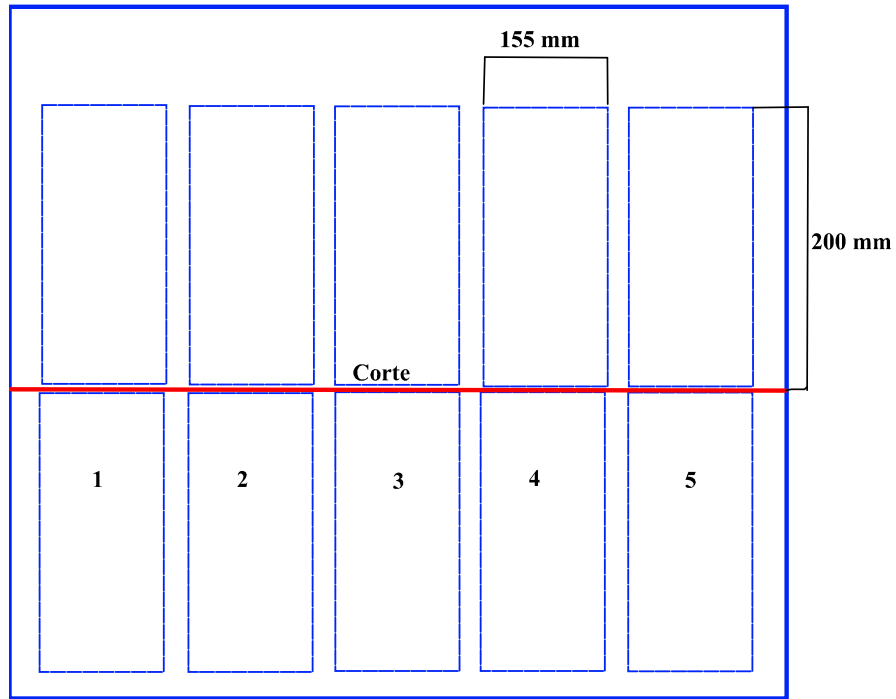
Esquema de la fabricación de probetas para soldadura.
